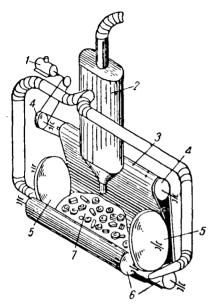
, Универсальный станок для одновременной обработки разнотипных изделий:
